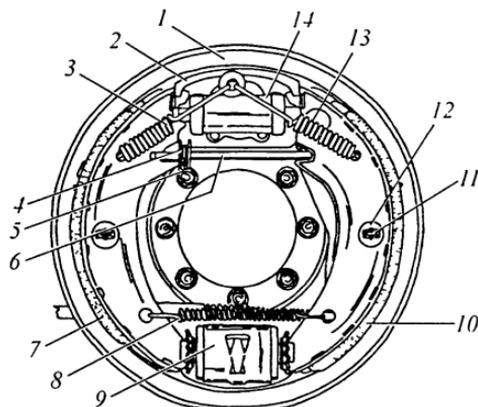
Тормозной механизм заднего колеса с регулировочным механизмом производства фирмы Mercedes-Benz: 1 — плата тормозного шита; 2 — опорная переключка; 3, 8, 13 — возвратные пружины; 4, 12 — опоры пружин; 5 — нажимная пружина; 6 — нажимная планка; 7 — пассивная (отжимаемая) тормозная колодка; 9 — регулировочный механизм тормозных колодок; 10 — активная (прижимаемая) тормозная колодка; 11 — анкерный штифт тормозной колодки; 14 — колесный тормозной цилиндр
